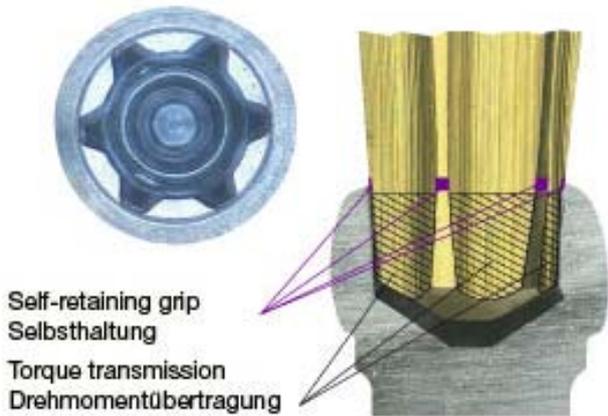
Schraubengewinde "Hexadrive" von Medartis
